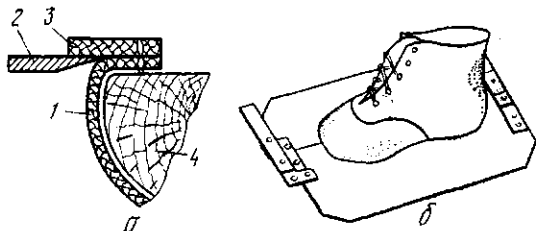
Схема затяжки пластинами (а) заготовки верха обуви метода крепления Парко-1 (б):
